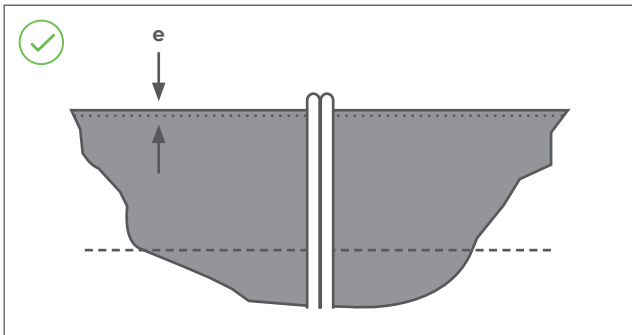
Schweißnaht mit gleichmäßiger Wulstausbildung (gut)
